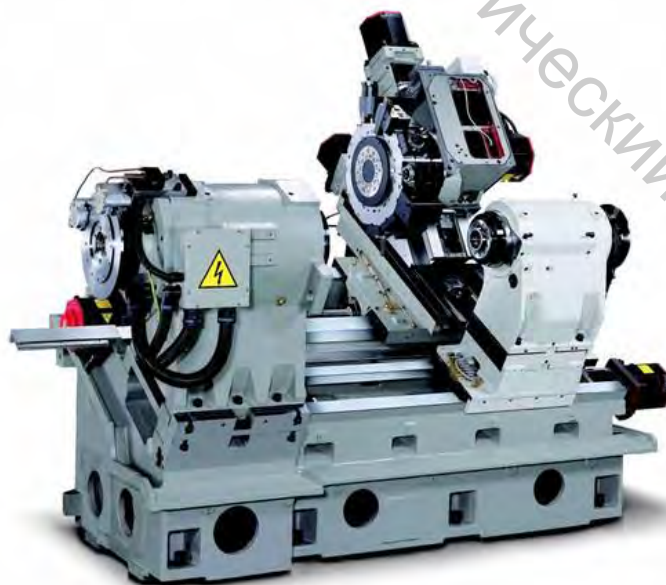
Компоновка токарного станка с ЧПУ
